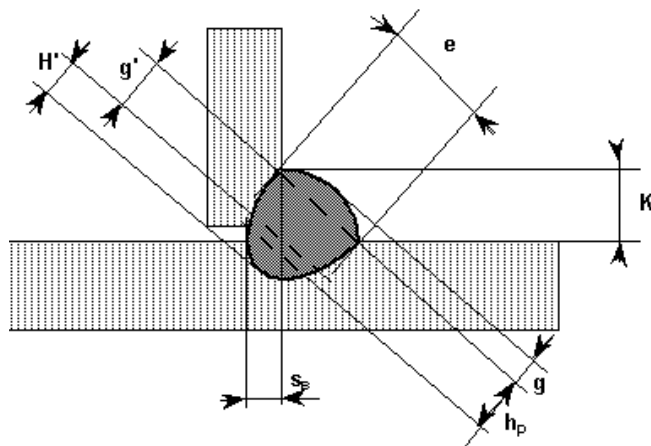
Геометрія для таврового зварного з'єднання.
